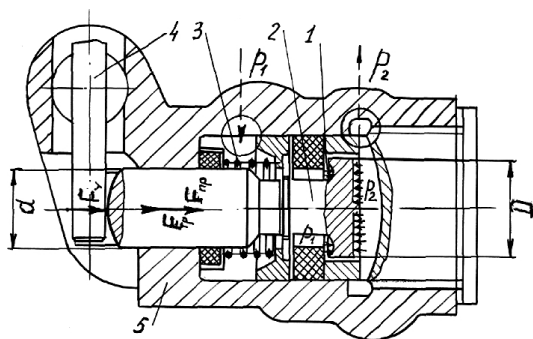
Регулятор тормозных сил с переменной точкой срабатывания автомобилей ВАЗ: 1 — клапан; 2 — ступенчатый поршень; 3 — пружина; 4 — торсион; 5 — корпус
